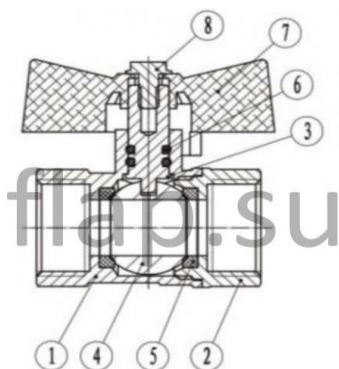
Чертеж крана с деталями из паспорта завода изготовителя
